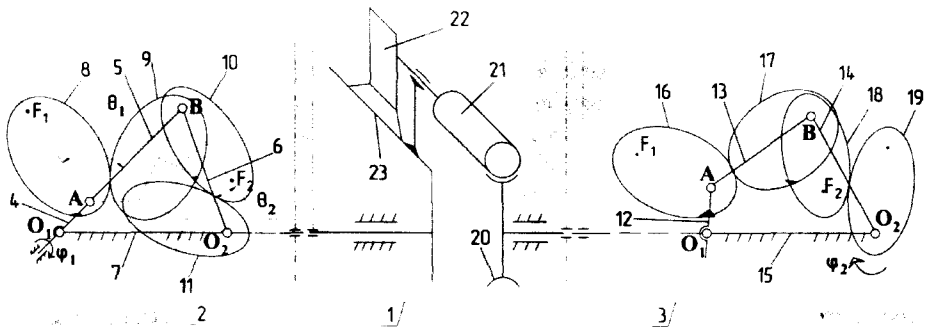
Регулируемый зубчато-рычажный привод периодического движения
